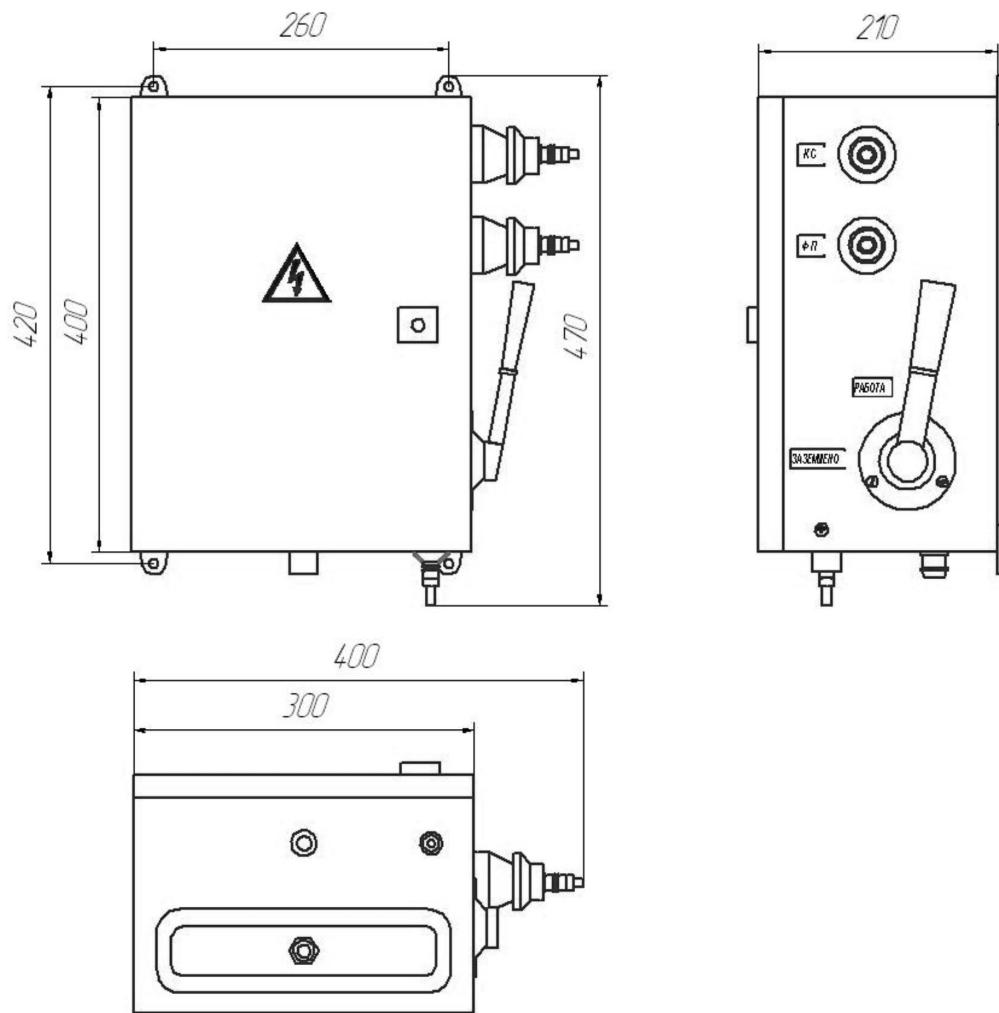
Габаритно-присоединительный чертеж ШОН.
